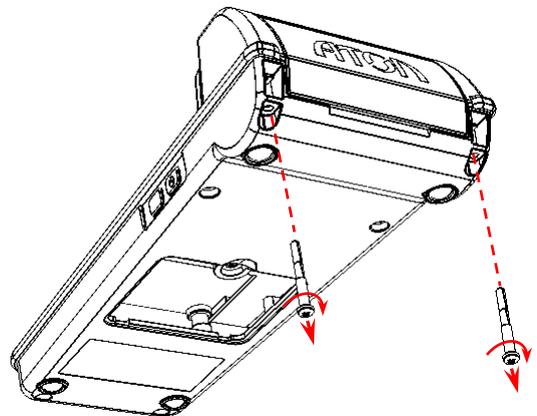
Демонтаж корпуса (открутить винты в нижней части корпуса)
